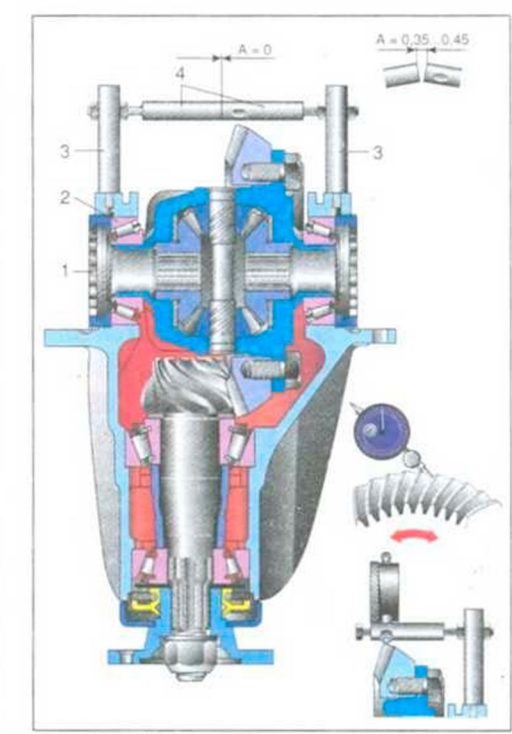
Приспособление для контроля предварительного натяга подшипников дифференциала: 1 — регулировочная гайка; 2 — подшипник; 3 — стойка приспособления; 4 — стержни
